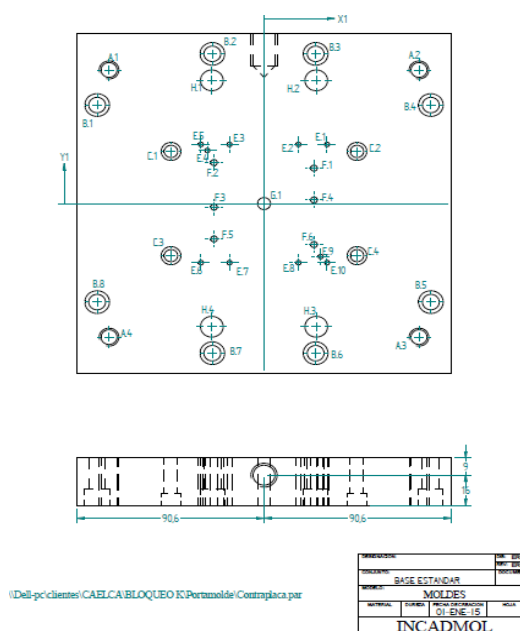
Contra placa, molde de inyección. Autor Incadmol S.A.
